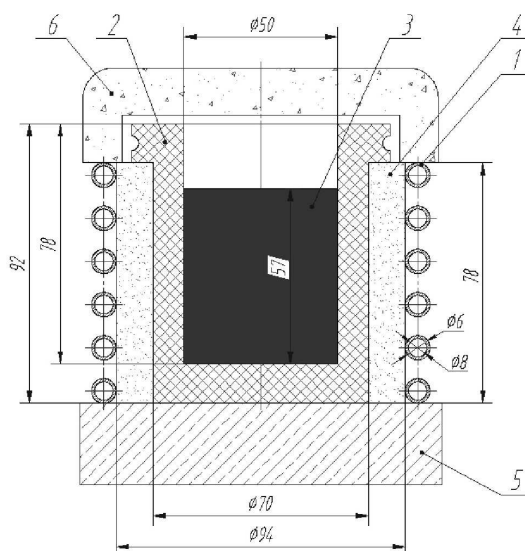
Чертеж системы «индуктор — загрузка» печи с футеровкой:
